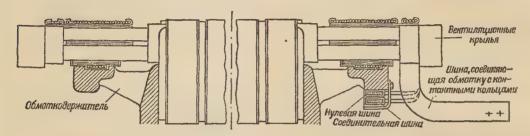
Продольный разрез ротора с волновой двухслойной обмоткой.
